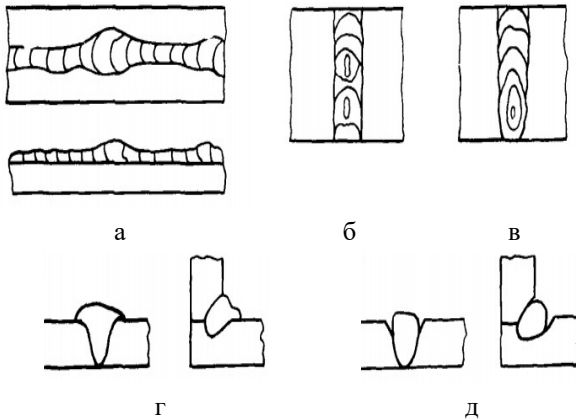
Зовнішні дефекти зварних швів: а – нерівномірна ширина шва; б – пропали; в – кратер; г – напливи; д – підрізи
